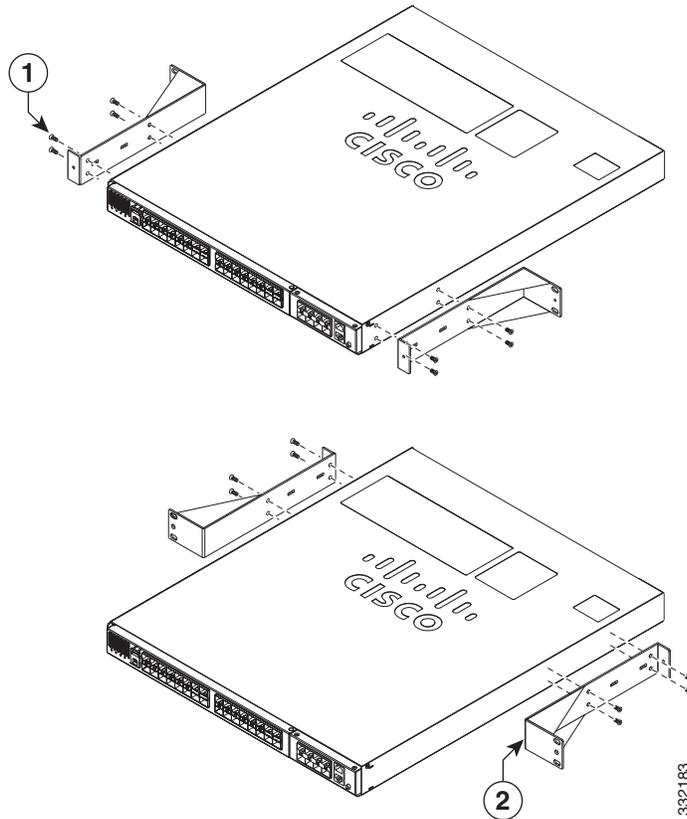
Снятие стандартных крепежей для монтажа в стойку с корпуса
